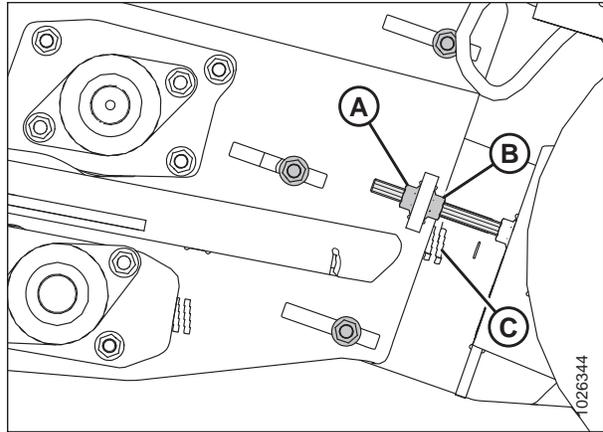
Calibrador del indicador de posición escalonado del lado derecho
